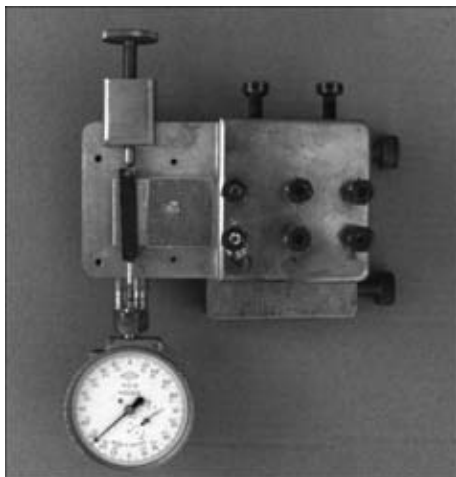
Загальний вигляд навантажувального пристрою для визначення діаметра ядра зварної точки з використанням механічного навантаження
